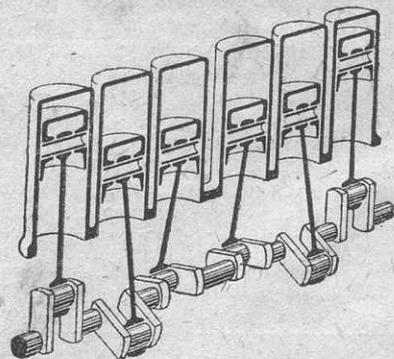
Схематическое изображение шестицилиндрового двигателя.
